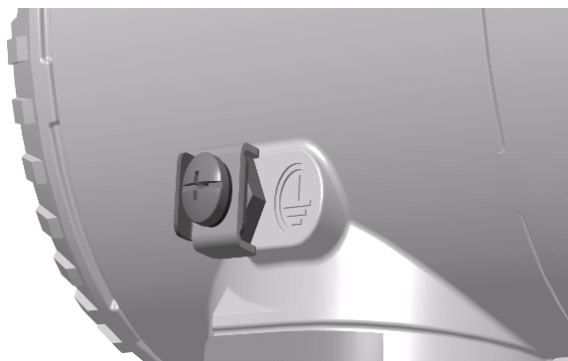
Клемма заземления на корпусе измерительного преобразователя
